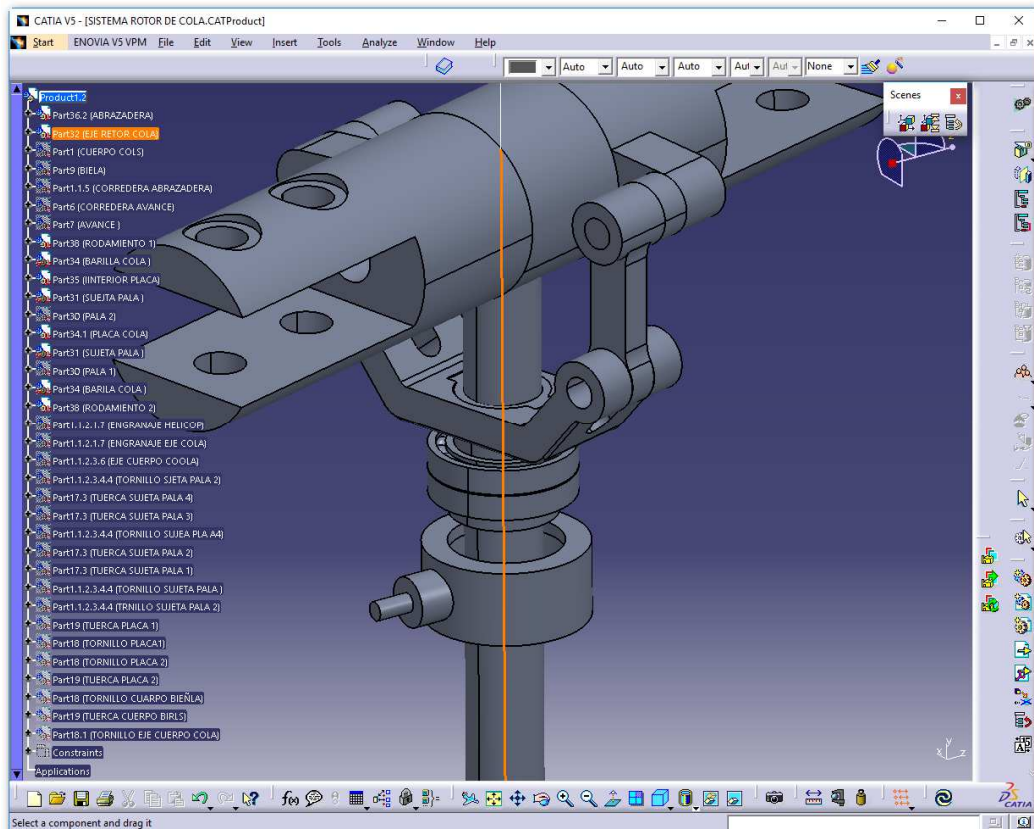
Montaje de placa – rodamientos – abrazadera 2.
